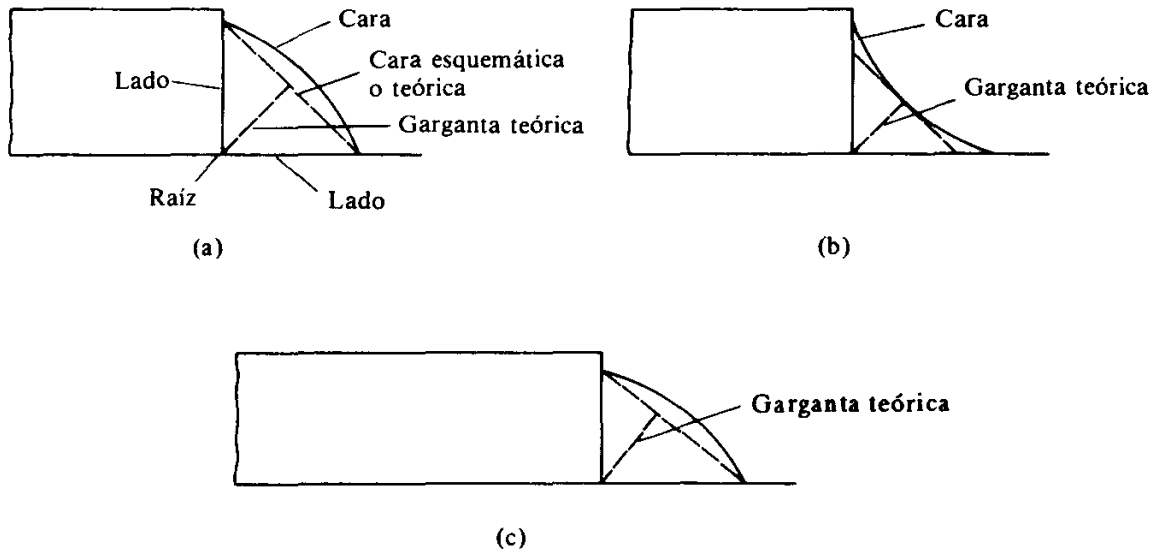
(a) Superficie convexa. (b) Superficie cóncava. (c) Soldadura de filete de lados desiguales.
